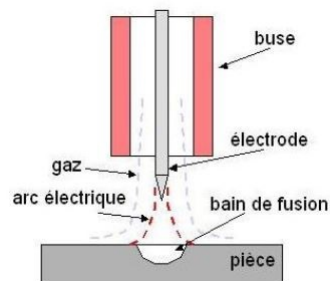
Principe du soudage TIG [Chapuis, 2011]
